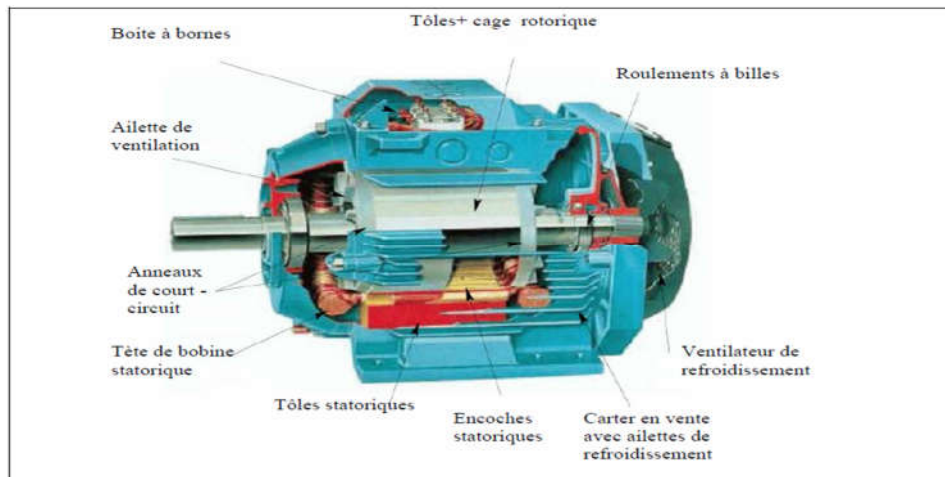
Éléments de constitution d'une machine asynchrone à cage d'écureuil [2].
